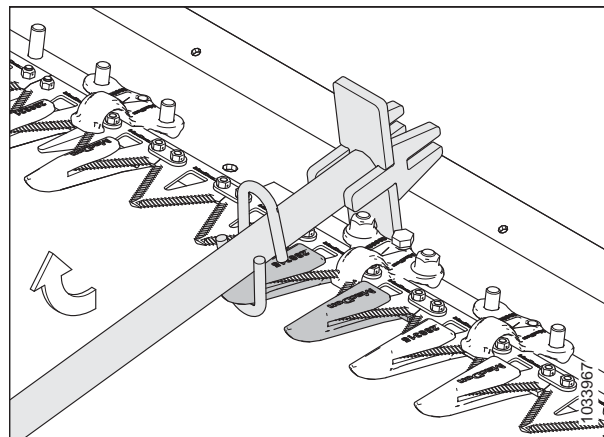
Регулировка смещением вверх — заостренный противорезущий палец
